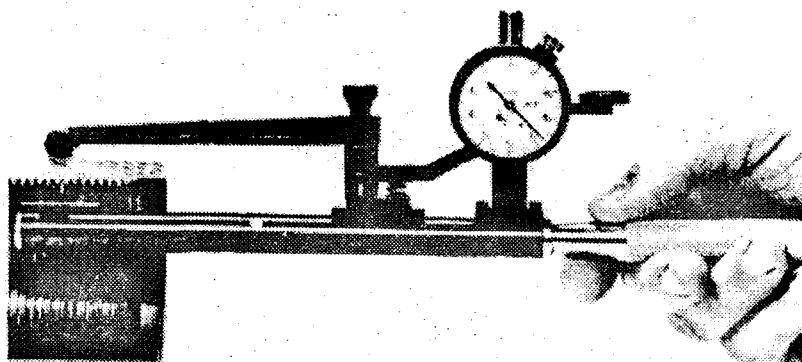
Калибр высоты резьбы для внутренней резьбы диаметром 3 дюйма и меньше (непрерывного типа с циферблатом)
